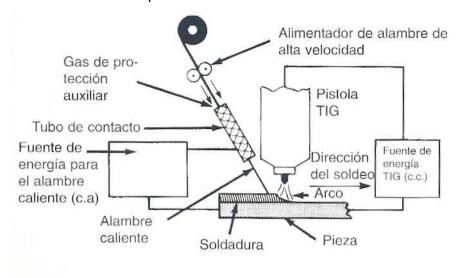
Instalación para soldeo TIG con alambre caliente²⁸
